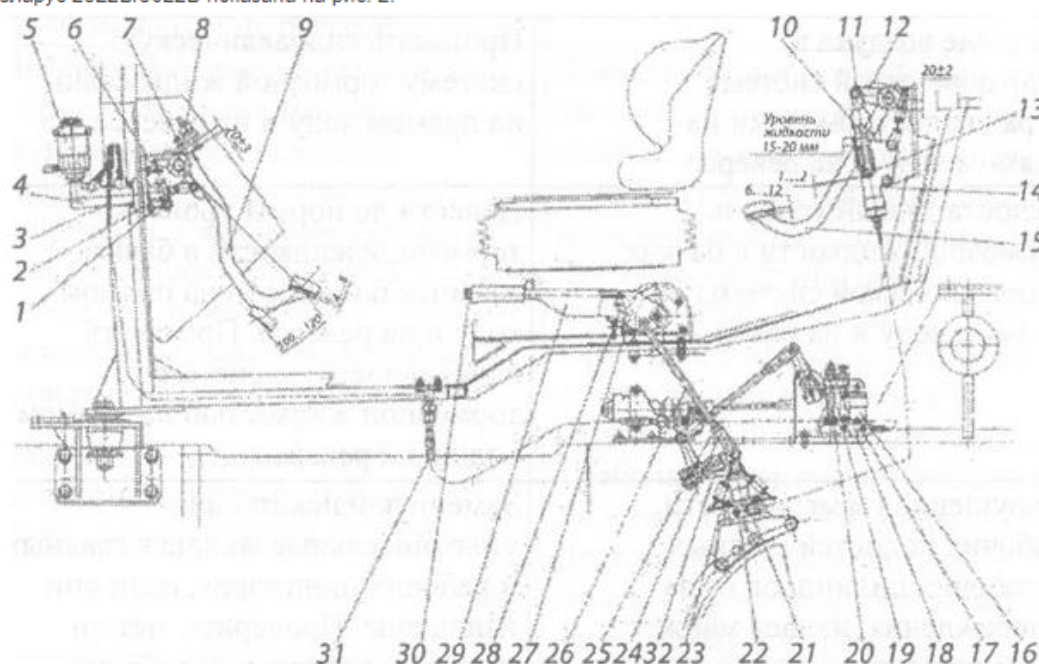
Схема управления тормозами тракторов Беларус 2522В/3022В: 1 — контргайка; 2 — толкатель; 3 — трубопровод; 4 — главный цилиндр; 5 — бачок; 6 — пружина; 7 — болт; 8 — гайка; 9 — педаль; 10 — толкатель; 11 — палец; 12 — вилка; 13 — поршень; 14 — главный цилиндр; 15 — педаль реверса; 16 — рабочий цилиндр; 17 — перепускной клапан; 18 — контргайка; 19 — регулировочная гайка; 20 — тяга; 21 — рабочий цилиндр реверса; 22 — перепускной клапан; 23 — палец; 24 — вилка; 25 — контргайка; 26 — тяга; 27 — сектор; 28 — фиксатор; 29 — рычаг; 30 — кнопка; 31 — рукав гибкий; 32 — рычаг
